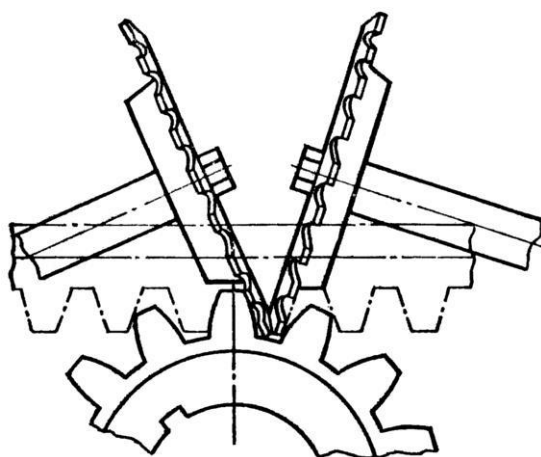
Фрезерування двома дисковими фрезами
